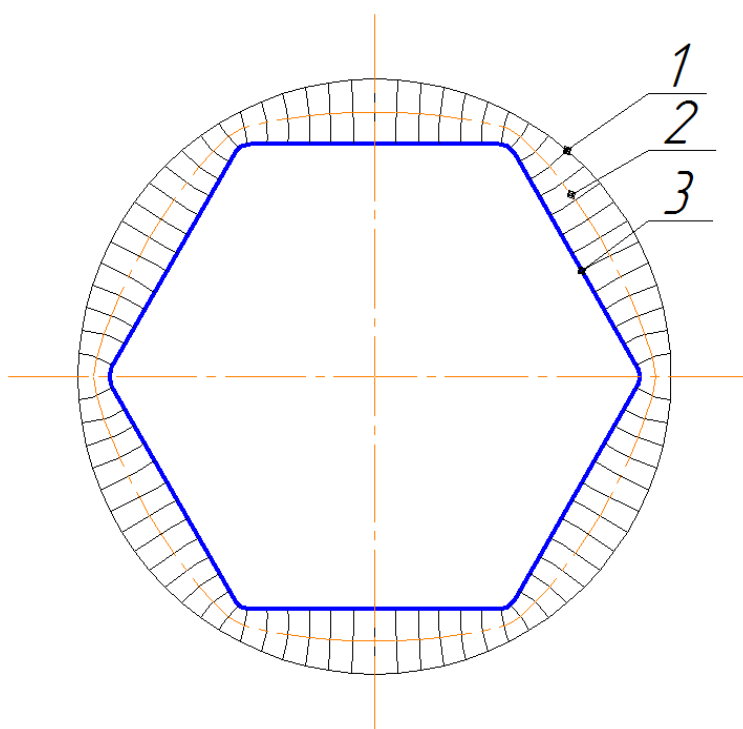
Контуры поперечного сечения внутренней поверхности заготовки 1 (тонкая линия), промежуточного перехода 2 (штрих-пунктир) и готовой трубы 3 (толстая линия). Наружные контуры заготовки и готовой трубы не показаны.
